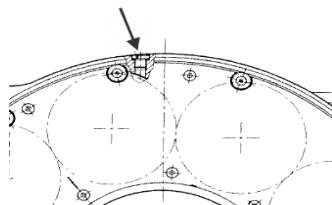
Cutia de viteze-turela cu scule antrenate=Live-tooling Turret Gear Box
